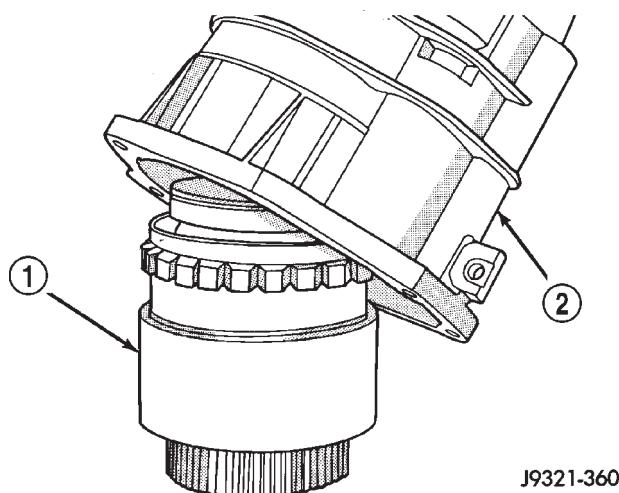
Desmontaje de la caja de transmisión del conjunto del tren de engranajes
